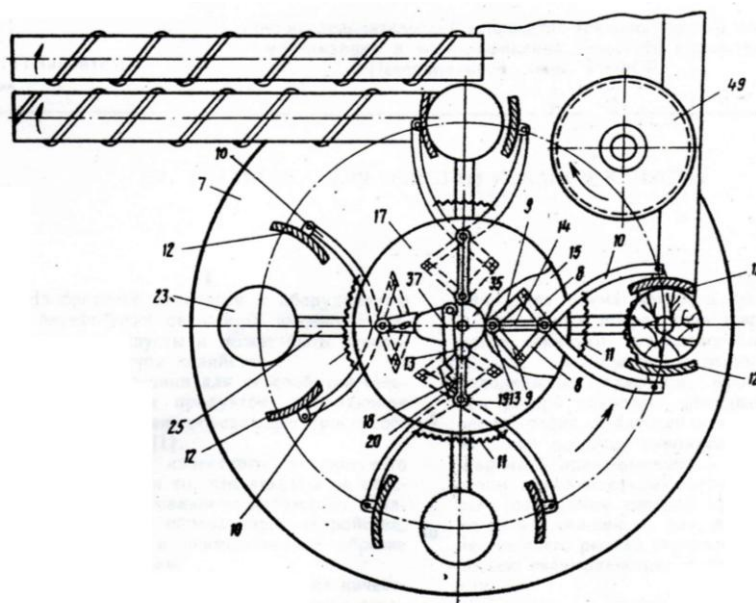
Пристрій зверху, загальний вигляд
